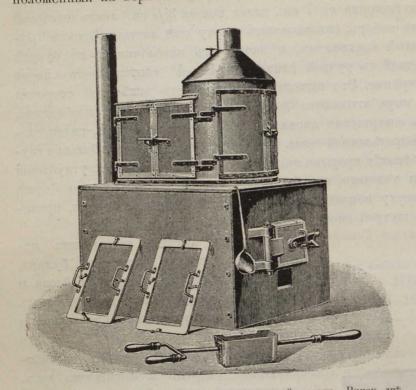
Очагъ для плавленія гарта и супильный шкапъ. Внизу двъ рамки для зажиманія матрицъ; на очагъ виситъ ложка для черпанія металла и внизу особой формы котелокъ съ рукоятками для наливанія въ него расплавленнаго гарта.
